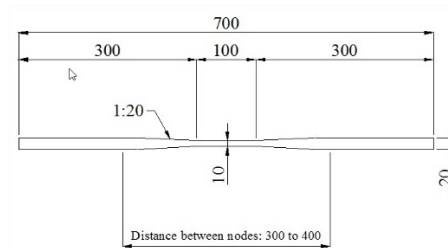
Pieza de prueba para ensayos de tensión. Dimensiones en mm.
